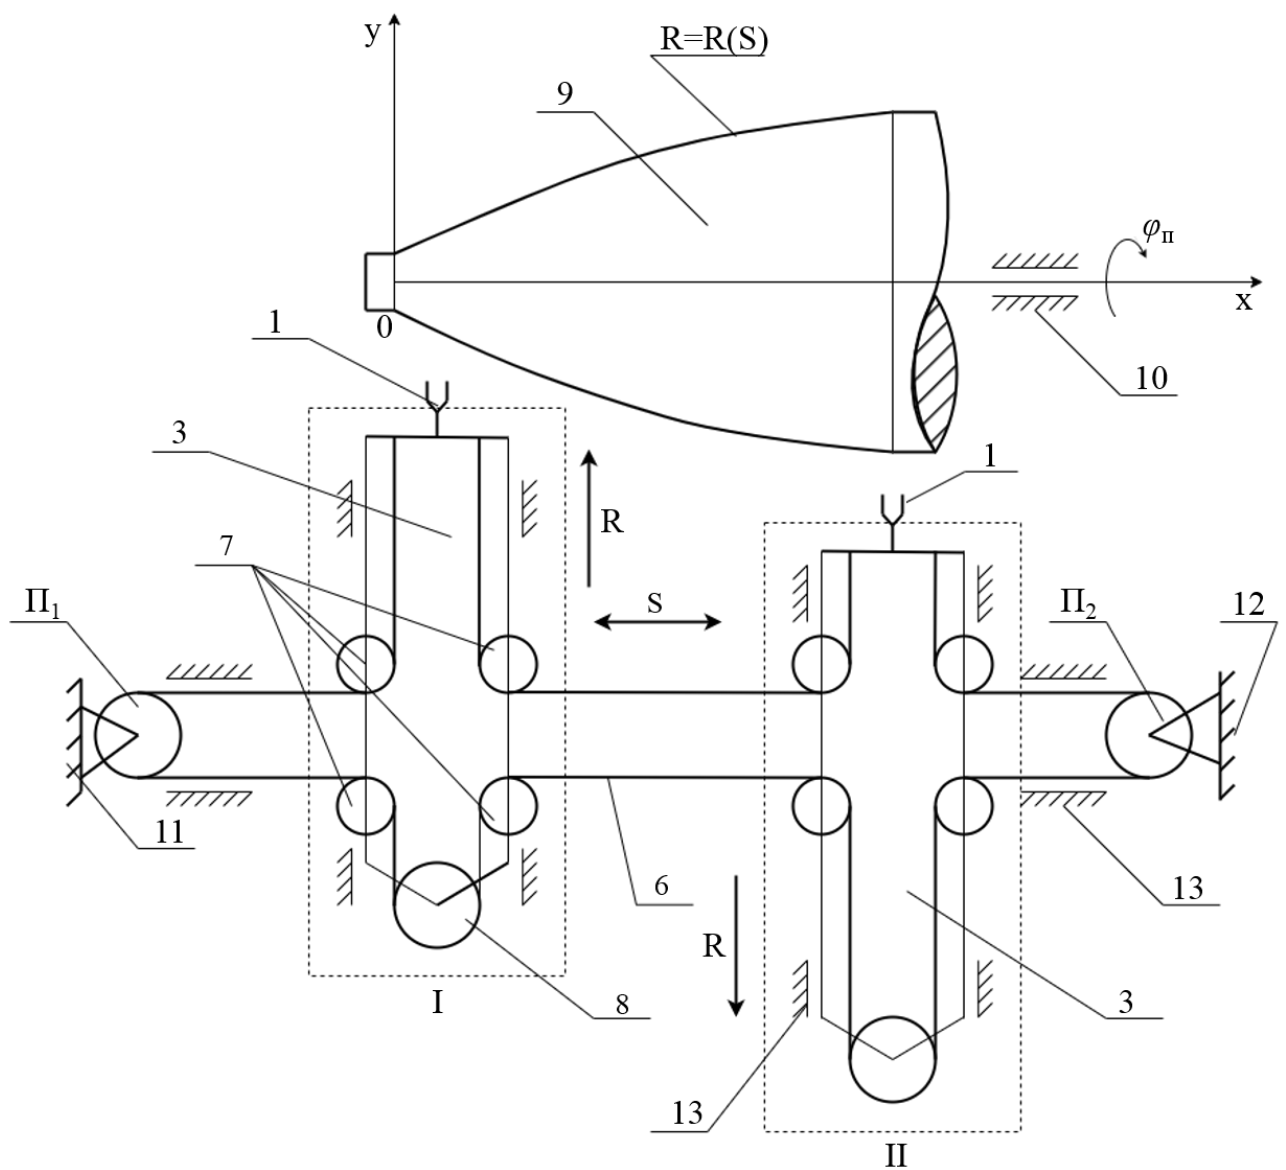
Схема работы механизма раскладки нити вдоль образующей паковки заданной кривизны.
